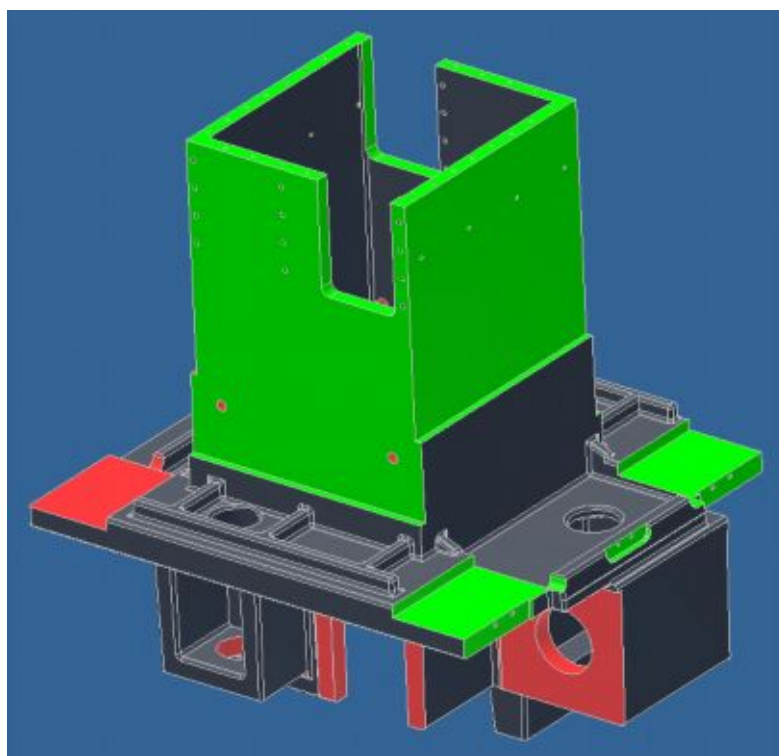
Vyhrubovaný odlitek po upnutí č.4
